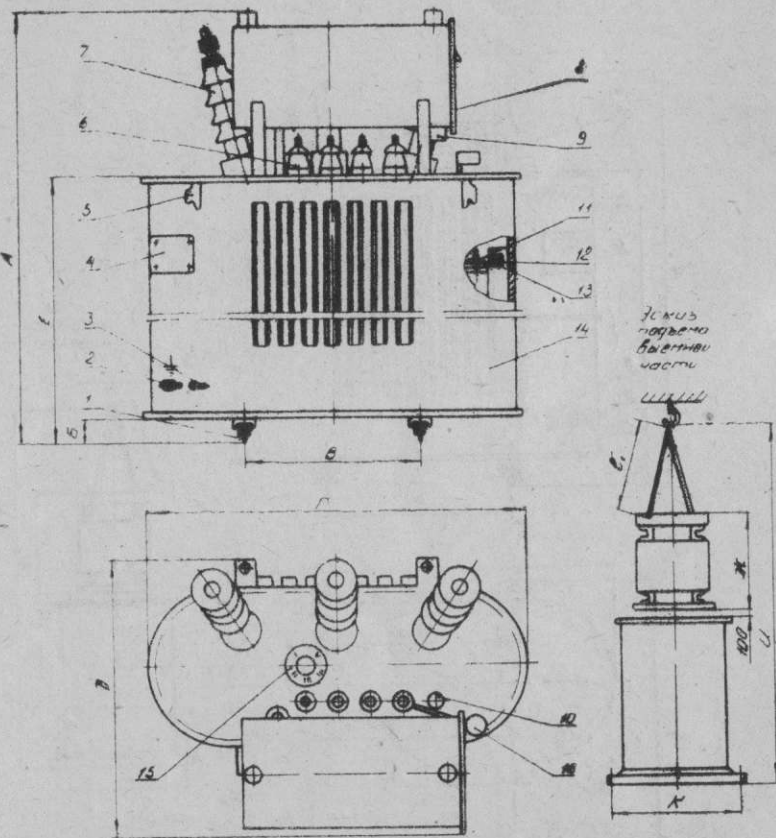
1-ролик транспортный; 2-заземление; 3-пробка для заливки и отбора пробы масла; 4-щиток мощности; 5-крюк для подъема трансформатора; 6-ввод НН; 7-ввод ВН; 8-маслоуказатель; 9-воздухоосушитель; 10-ртутный термометр; 11-гайка; 12-скоба; 13-пластина; 14-бак; 15-переключатель; 16-предохранитель (устанавливается по требованию заказчика).
